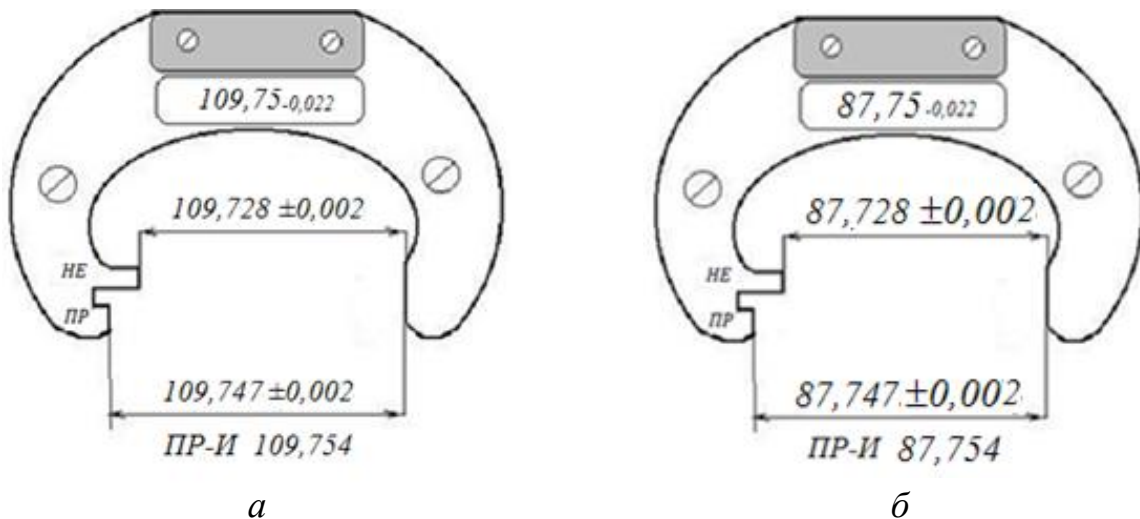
Эскиз калибра-скобы для контроля размера шейки коленчатого вала двигателей ЯМЗ после шлифовки под ремонтный размер: а) коренной; б) шатунной
